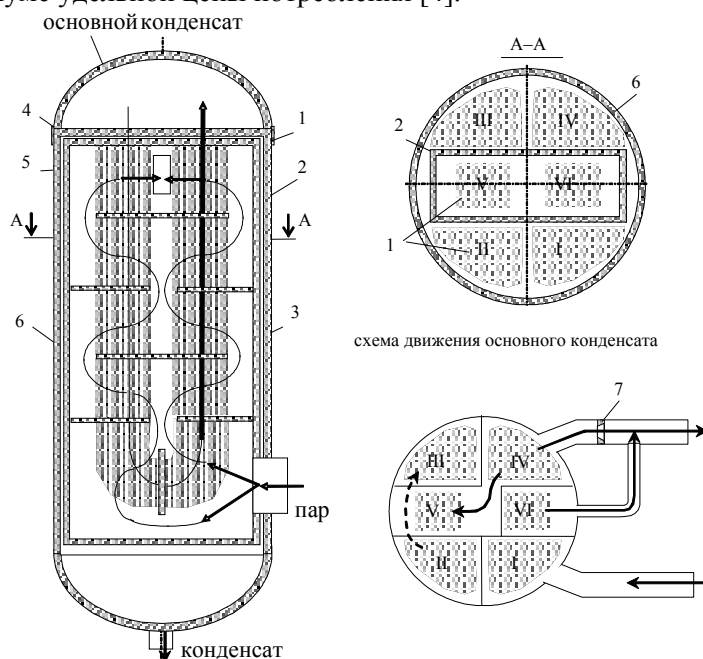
Подогреватель с ОП в центре трубного пучка: 1 — трубный пучок, 2 — кожух ОП, 3 — промежуточная перегородка, 4 — трубная доска, 5 — окна для выхода пара, 6 — корпус подогревателя, 7 — дроссельная шайба, I, II, III, IV, V, VI — ход основного конденсата
